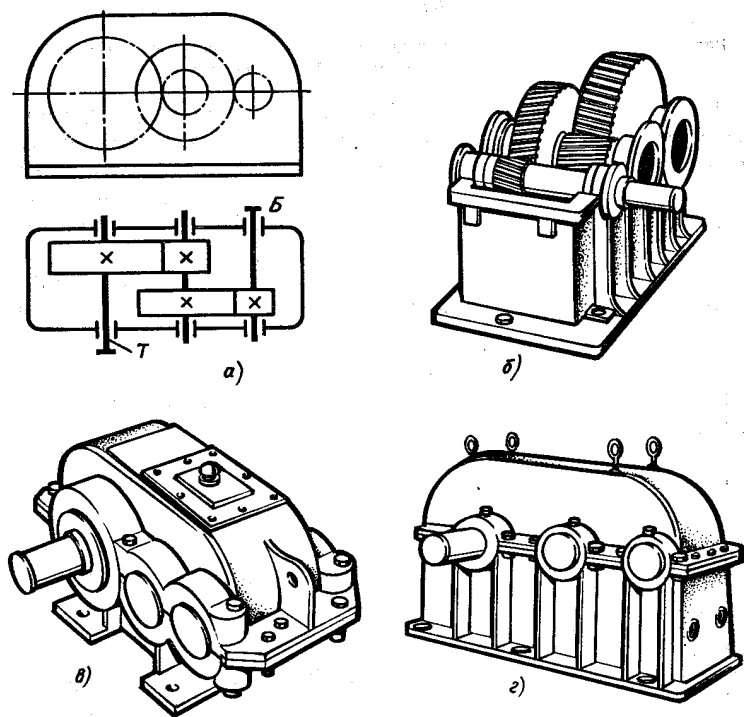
Двухступенчатый горизонтальный редуктор с цилиндрическими колесами: а — кинематическая схема; б — редуктор со снятой крышкой (колеса косозубые); в — общий вид редуктора, у которого подшипниковые узлы закрыты врезными крышками; г — общий вид редуктора, у которого подшипниковые крышки привернуты винтами
